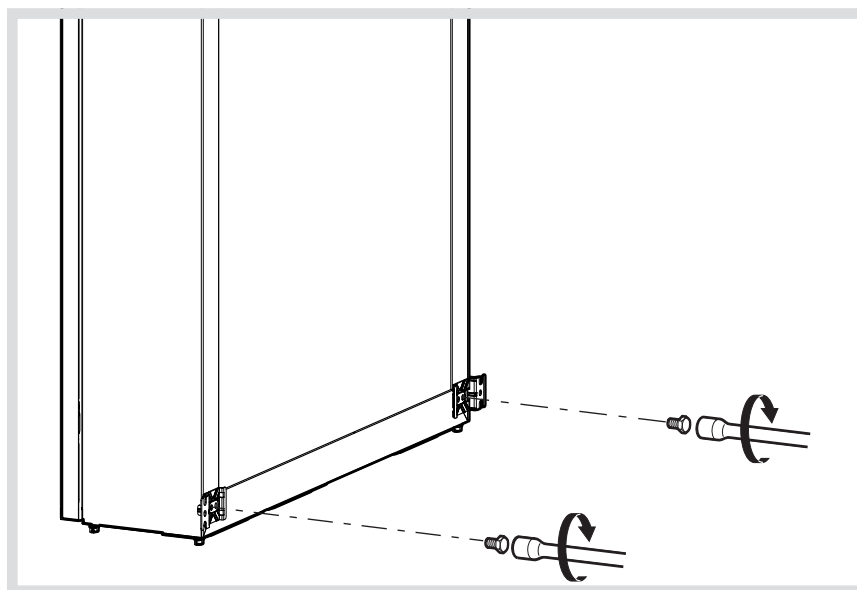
Montage Befestigungslaschen zur seitlichen Fixierung
